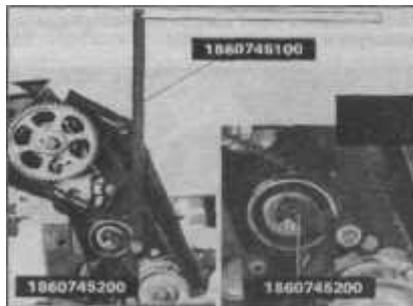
Специальные инструменты для регулировки натяжения зубчатого приводного ремня, установленные на шкиве механизма натяжения (Глава 16)
